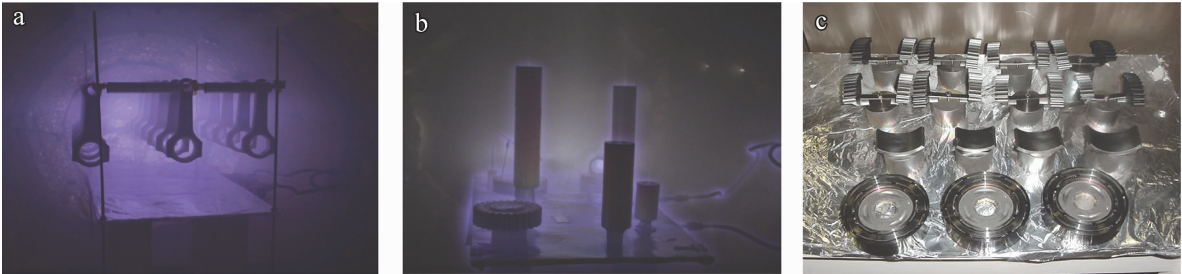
工件的 DLC 镀膜 (a)一次加工同种多个工件 (b)一次加工多种工件 (c)镀过 DLC 的工件
